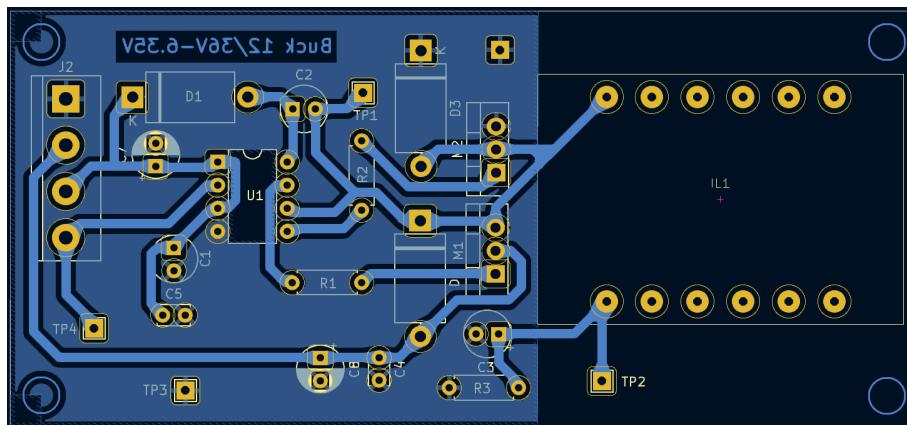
Diseño del PCB del *buck* en *Kicad*.
